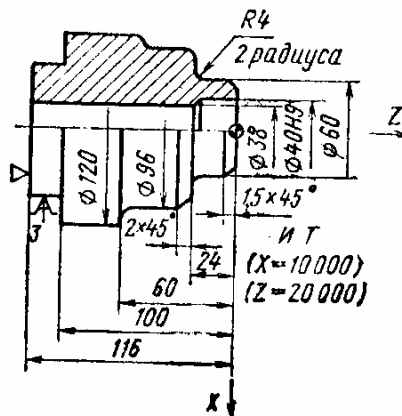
Эскиз заготовки (к задаче 16.12)
